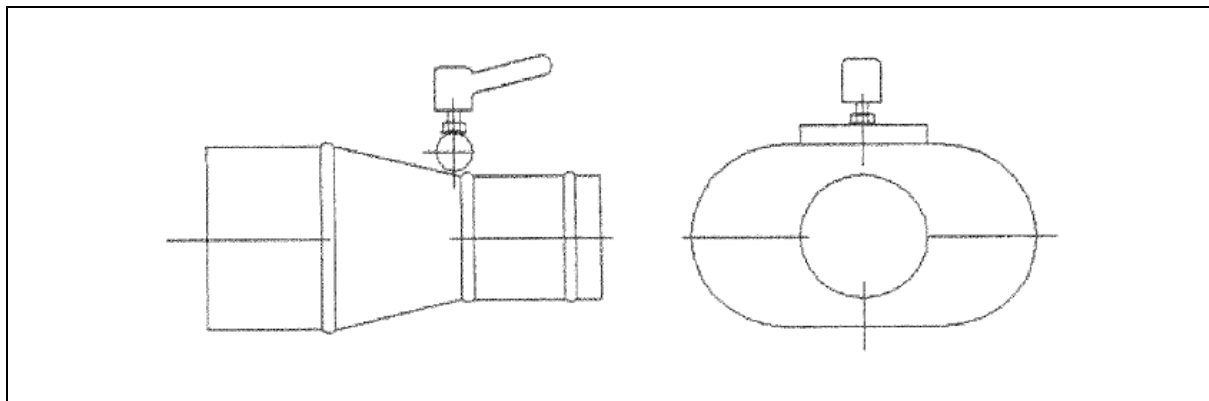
Darstellung Blechtülle oval mit Klemmschraube
